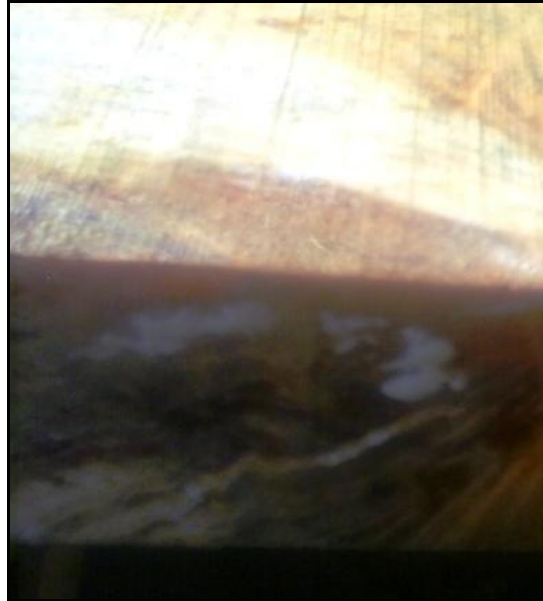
Bolsas de resina en la veta de la pieza aserrada.
